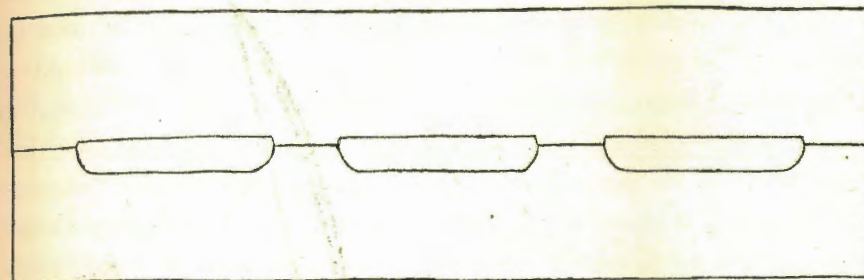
Coupe d'un moule en pierre pour couler les flans en chapelet.
